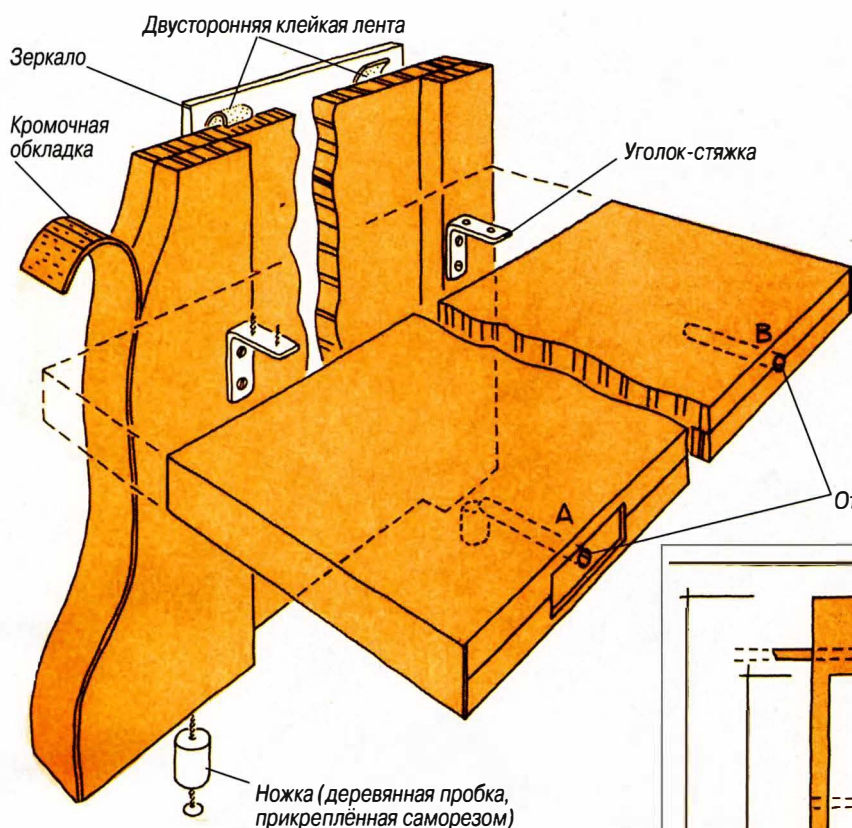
Все открытые кромки фасадной плиты и полок облицовывают мебельной обкладкой. Зеркало крепят двусторонней клейкой лентой.
